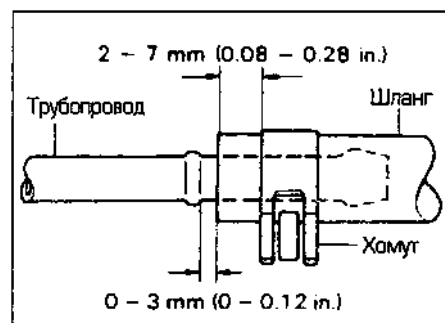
Соединение шланга с металлическим трубопроводом
